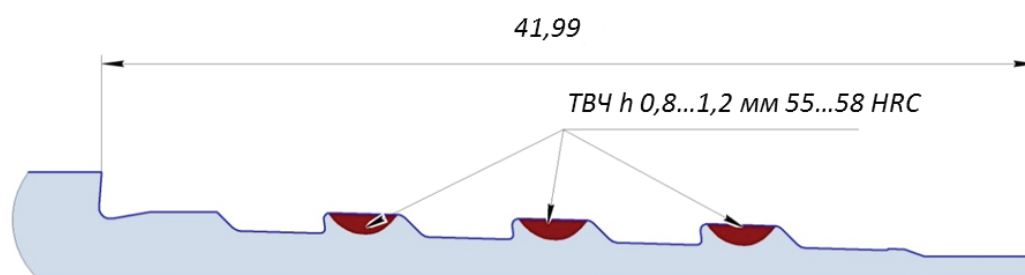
Эскиз расположения зоны ТВЧ на профиле резьбы
